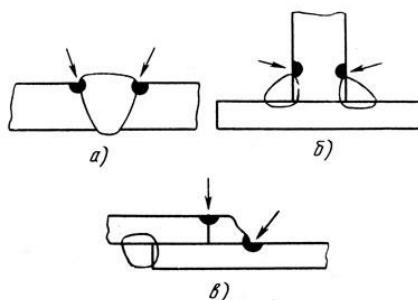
Подрезы зоны сплавления: а - стыкового, б - углового, в - нахлесточного
